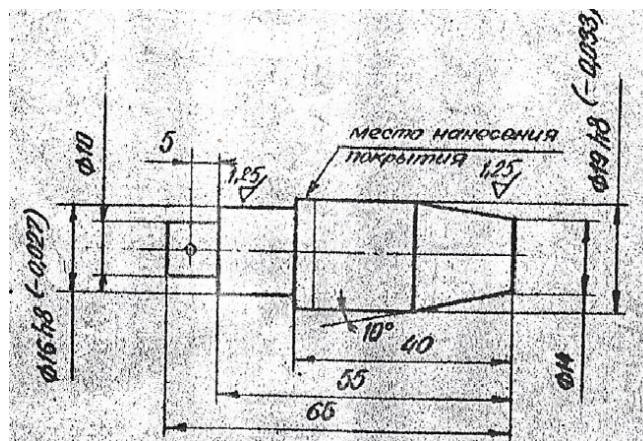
Образец для испытания прочности сцепления покрытия с основой
